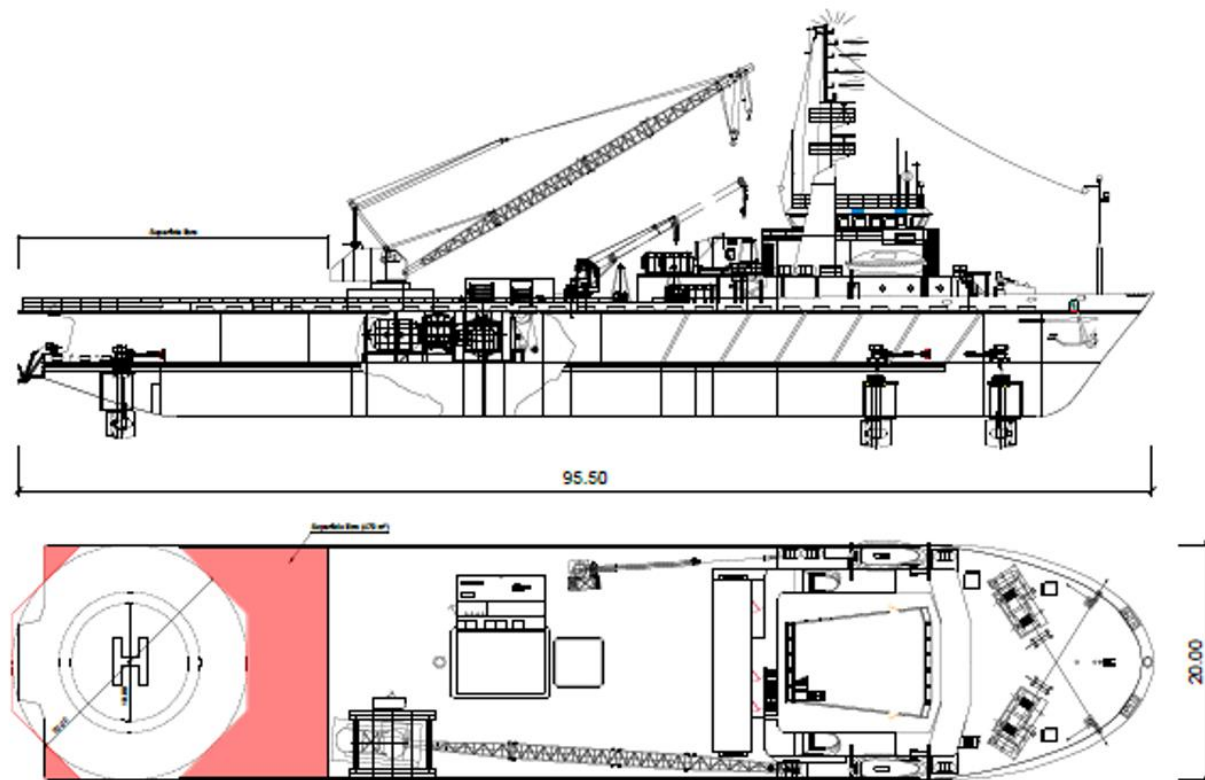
Alzado y planta del buque de apoyo marítimo para instalación del helipuerto. Fuente: Propia.
